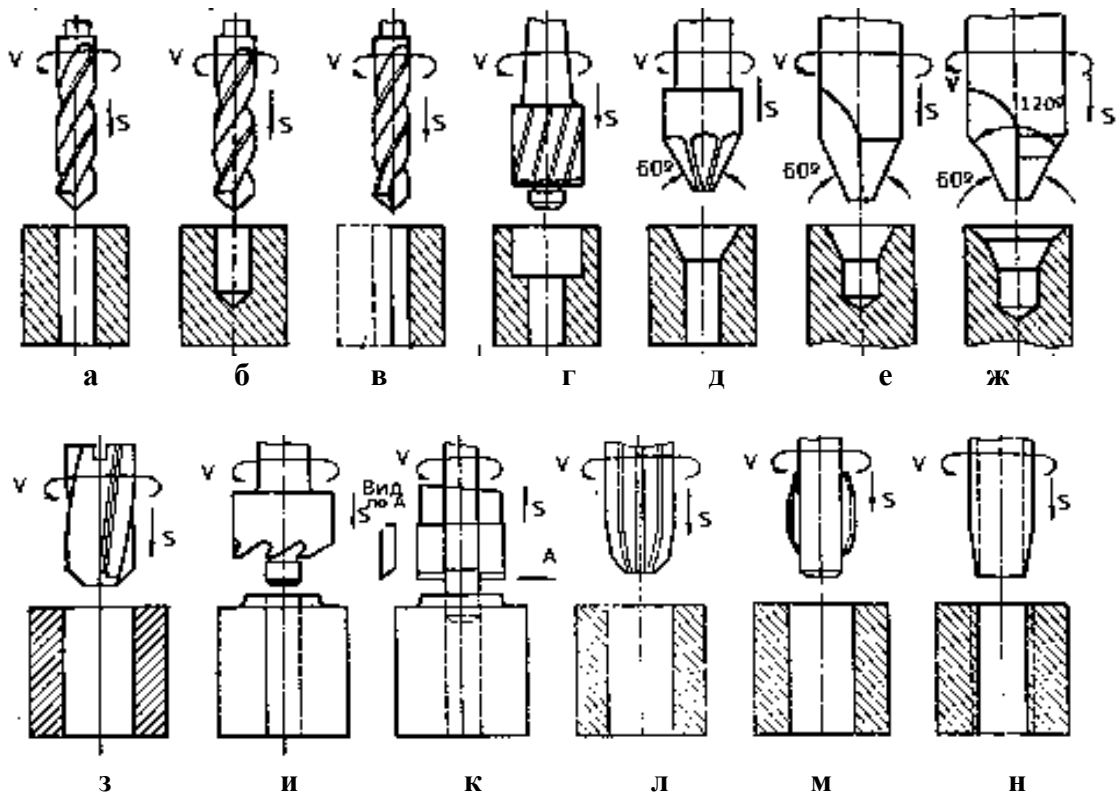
Типи обробки заготовок на свердильних станках
